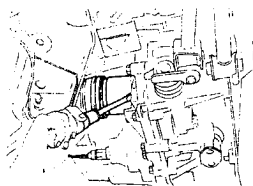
Отжимание левой полуоси от коробки передач – модели с механической коробкой передач (См. Раздел 3)
